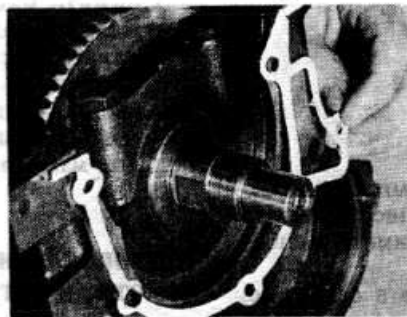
Установите новую прокладку маслонасоса на блоке цилиндров — двигатель 2,0 л с двумя распредвалами
